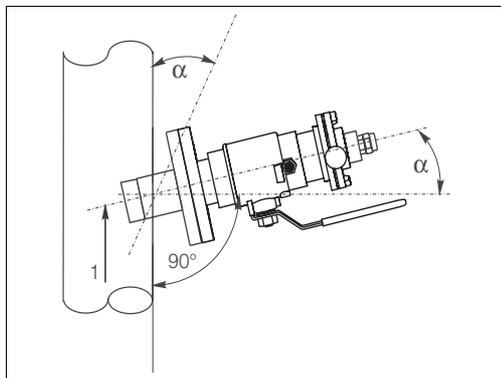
Montage sur conduite montante ou latéralement sur une cuve
